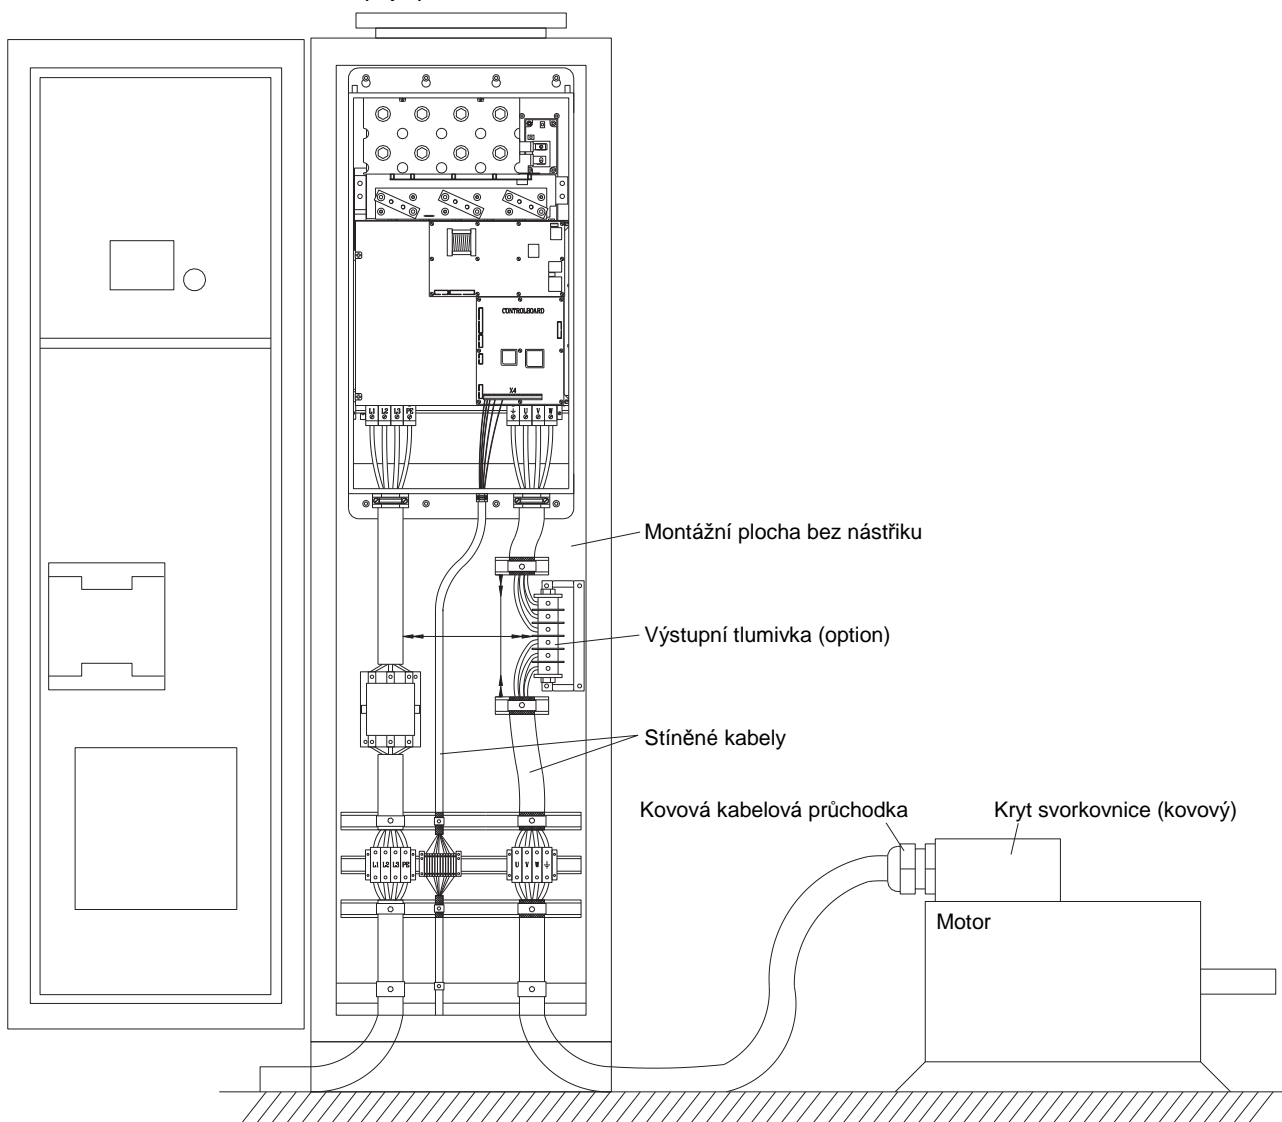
Montáž na izolovanou montážní desku nebo volné připojení bez montážní desky.
